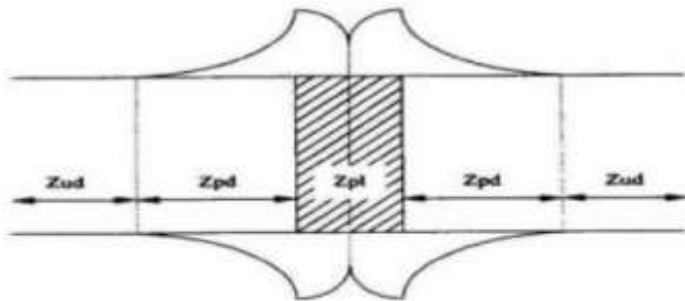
Skema *Inertia-drive welding
